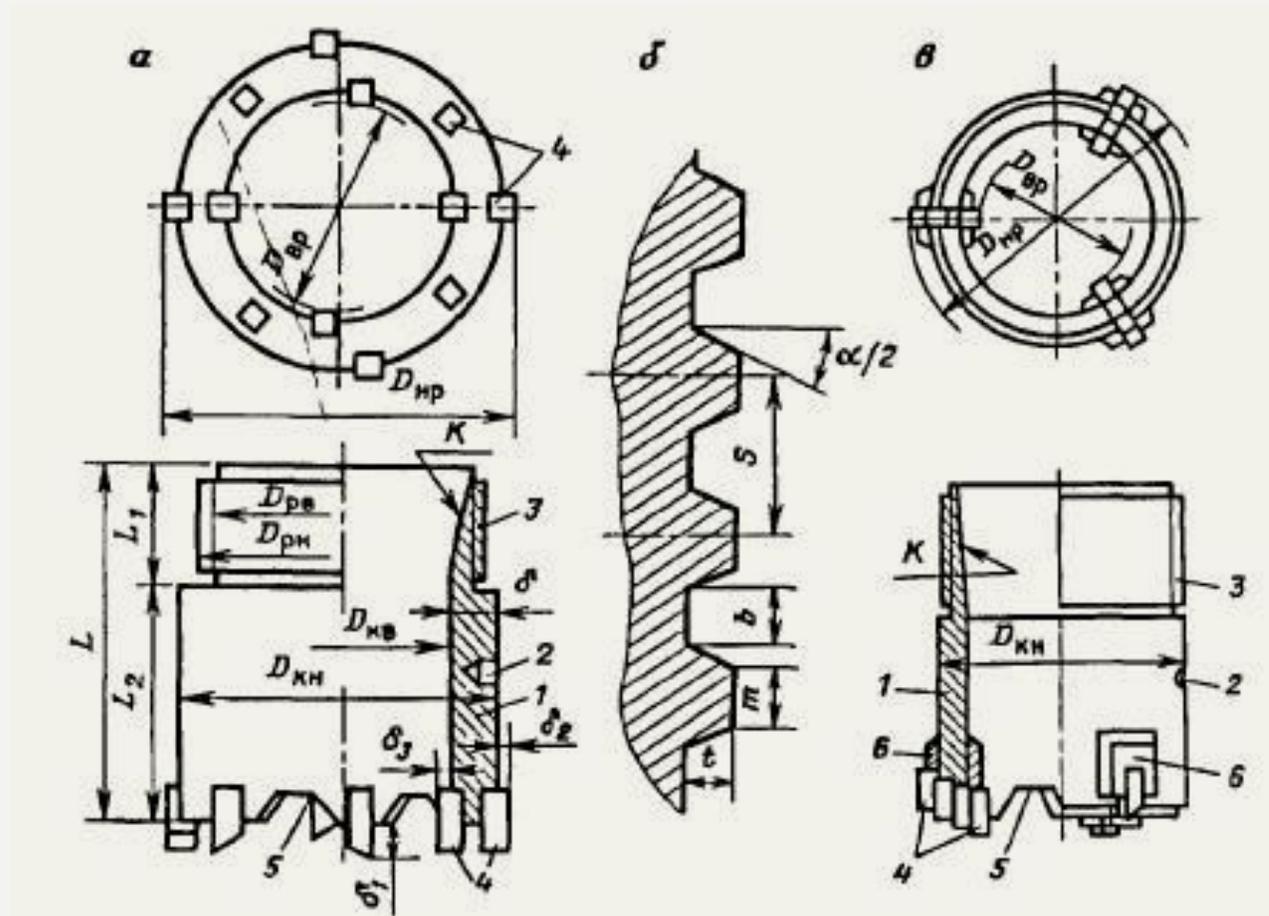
Конструктивные элементы твердосплавных коронок:
